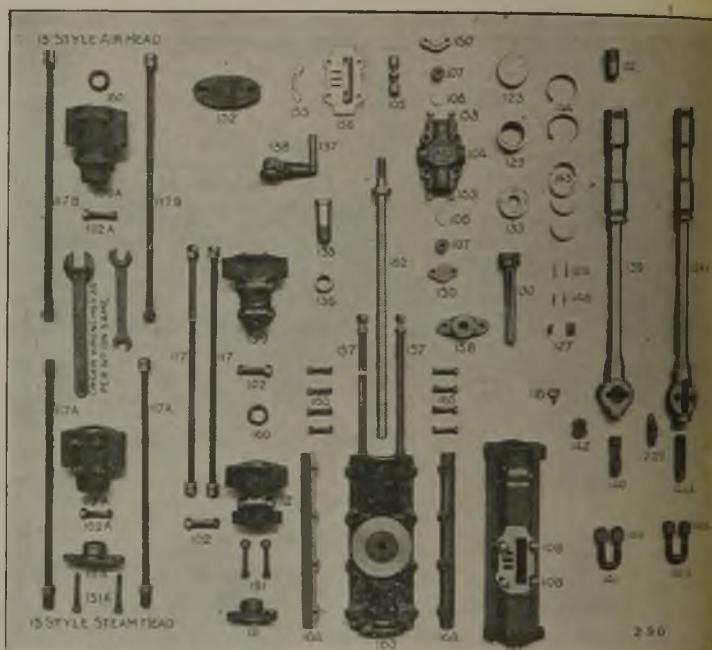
Hauptteile einer Ingersoll-Bohrmaschine.
